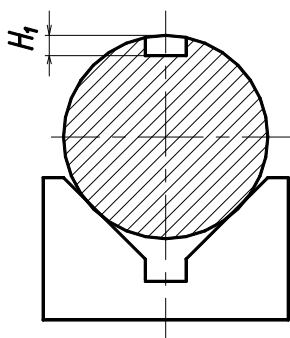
Базирование детали в призмах при фрезеровании шпоночного паза
